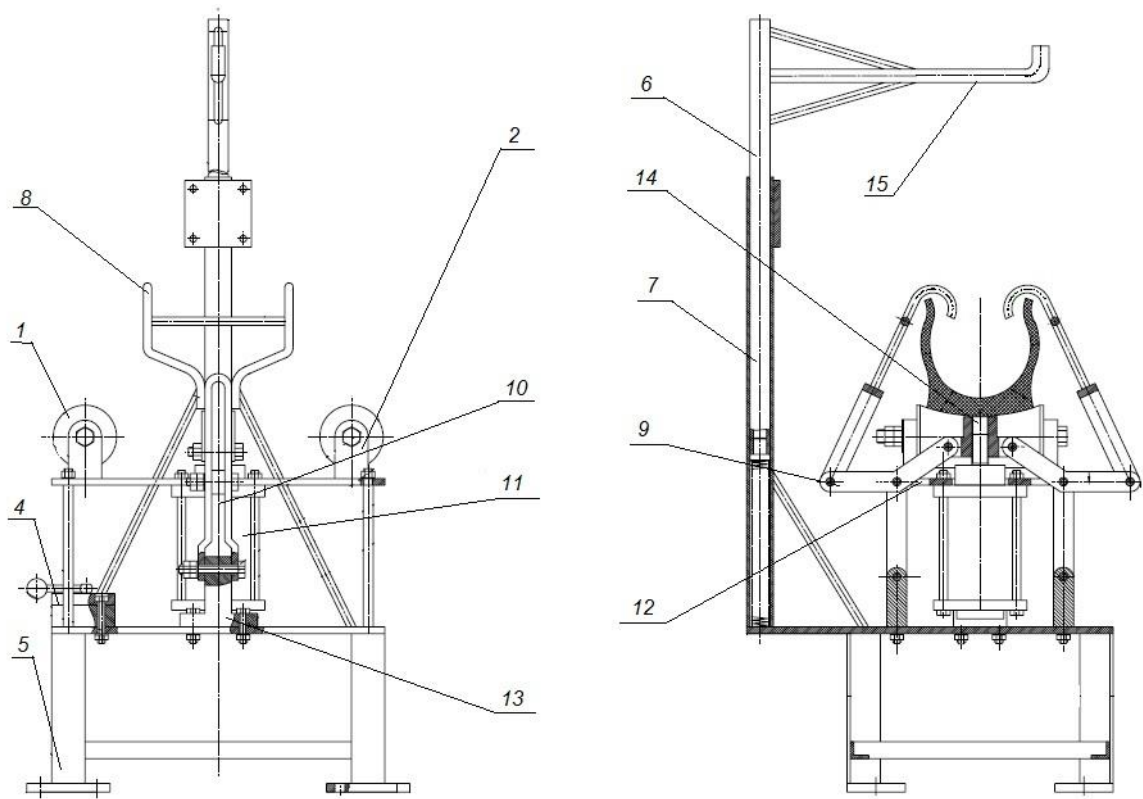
Стенд для огляду та ремонту шин: 1 – ролик; 2 – опора; 3 – стійка; 4 – розподільний кран; 5 – стіл; 6 – гачок; 7 – кронштейн; 8 – захват; 9 – важіль; 10 – тяга; 11 – пневмоциліндр; 12 – плита; 13 – опора; 14 – насадка; 15 – установочний гачок
